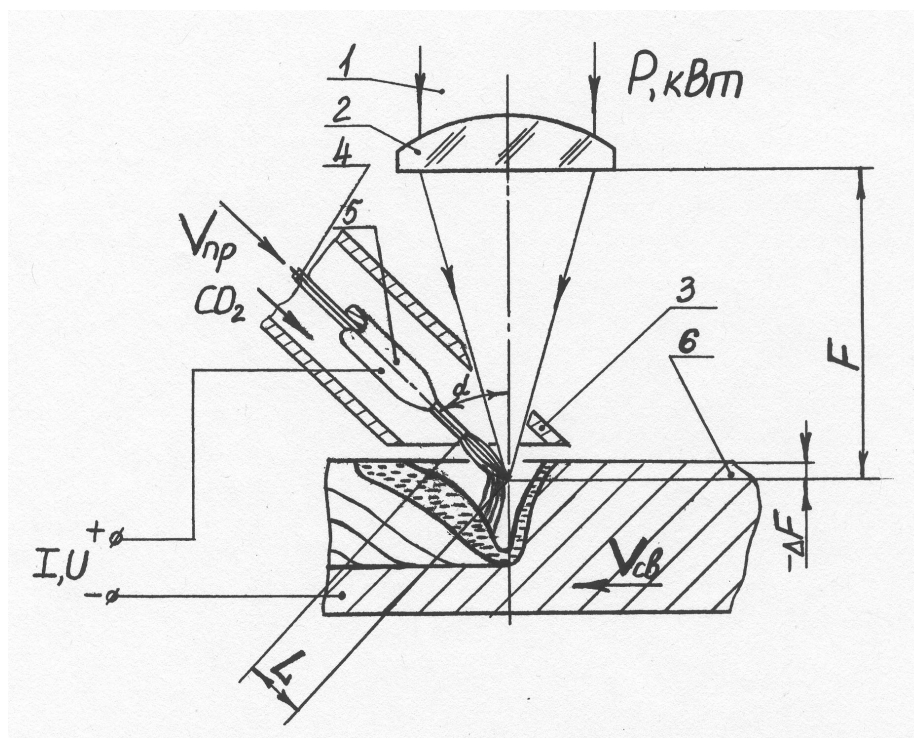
Схема гибридной лазерно-дуговой сварки.
